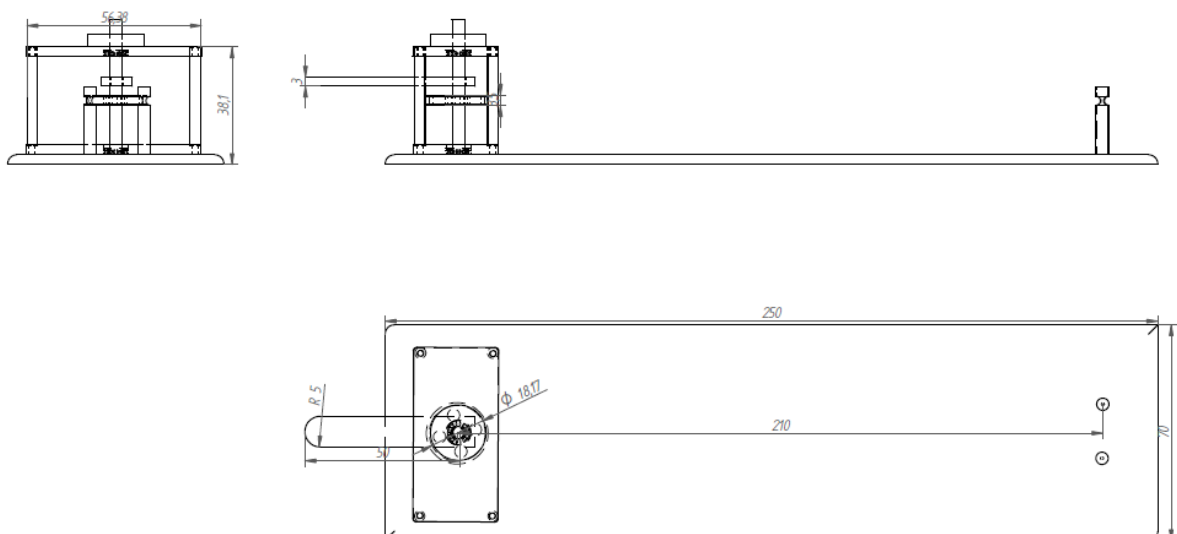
Plano detalle 2D. Alzado, planta y perfil de la estructura.
